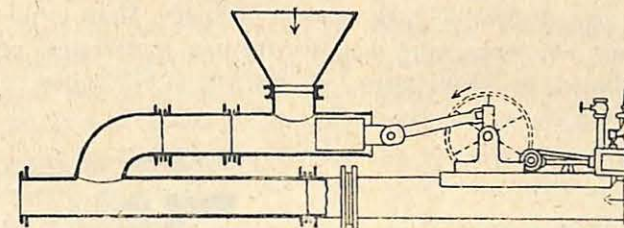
Coupe au travers de l'installation de chargement de Heringhaus.
